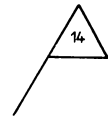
Zeichen für Bezifferung von Schweißnähten.
